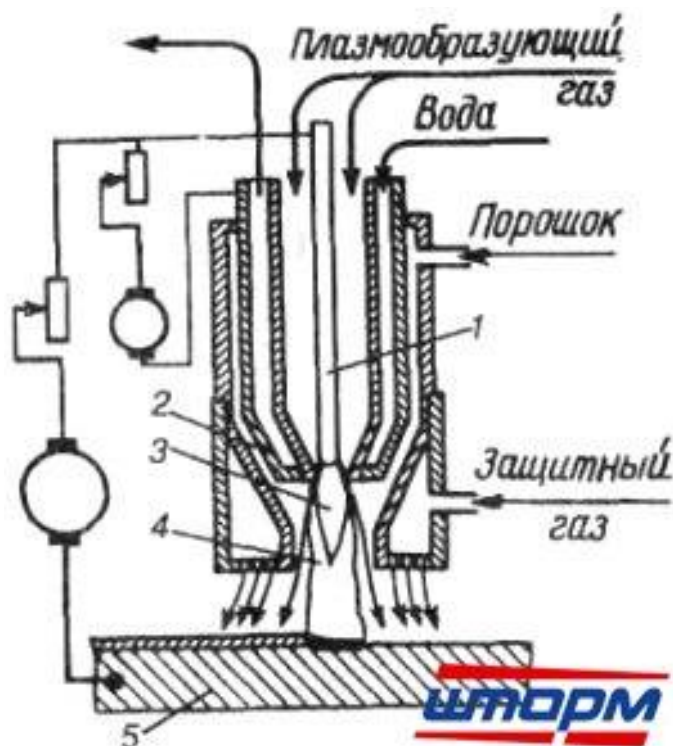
Схема плазменной наплавки с вдуванием порошка в дугу
